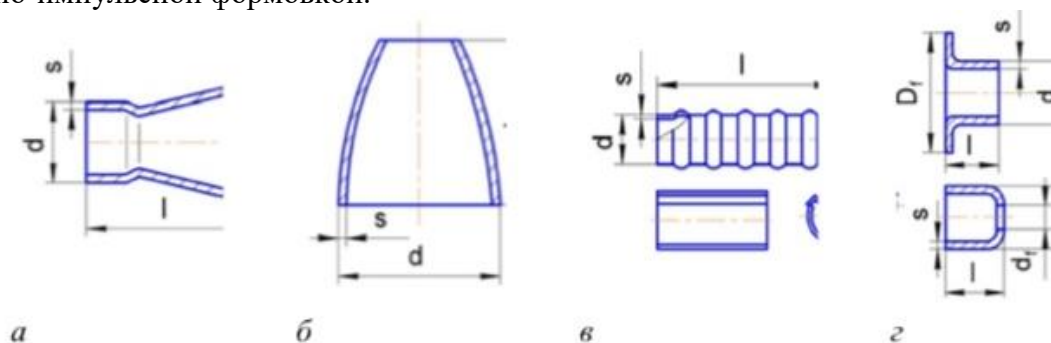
Типовые операции магнитно-импульсной формовки трубчатых заготовок. Особенностью изготовления переходников сложного контура является неравномерность деформации по периметру заготовки.
